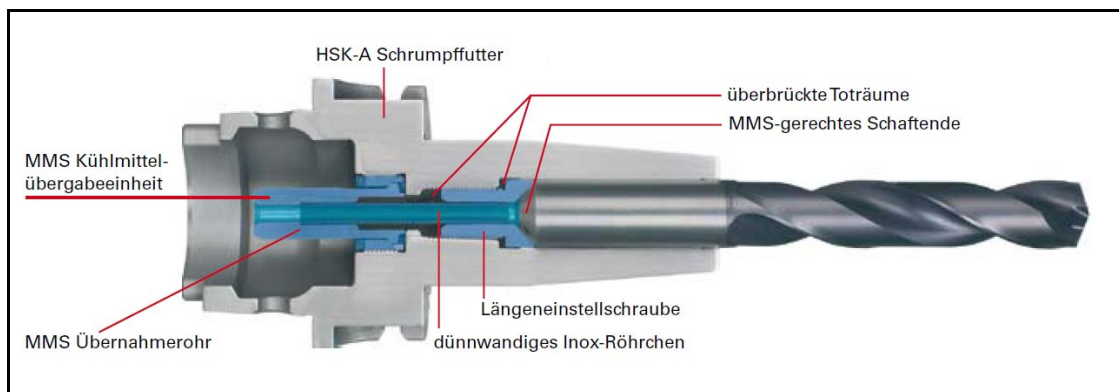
MMS gerechte Werkzeugaufnahme³⁸
